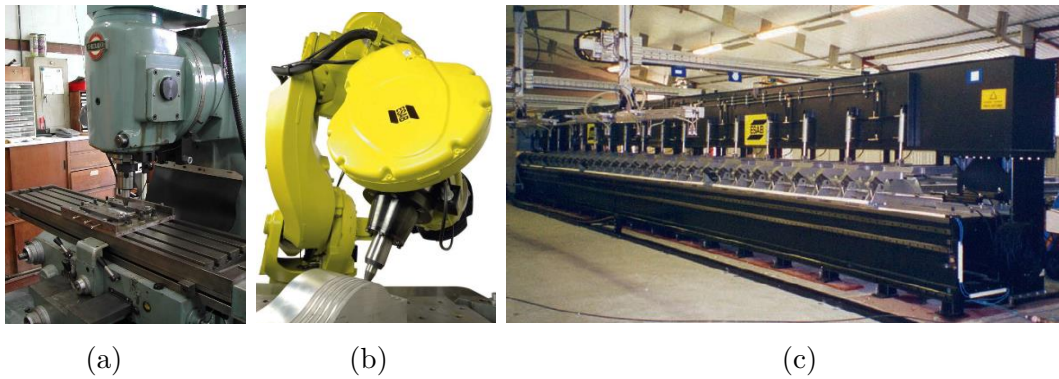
Types d'équipements utilisés pour le soudage FSW : (a) fraiseuse à commande numérique, (b) robot dédié au FSW et (c) installation industrielle de type portique. Photos tirées de [Besharati Givi+2014; ESAB2011].
